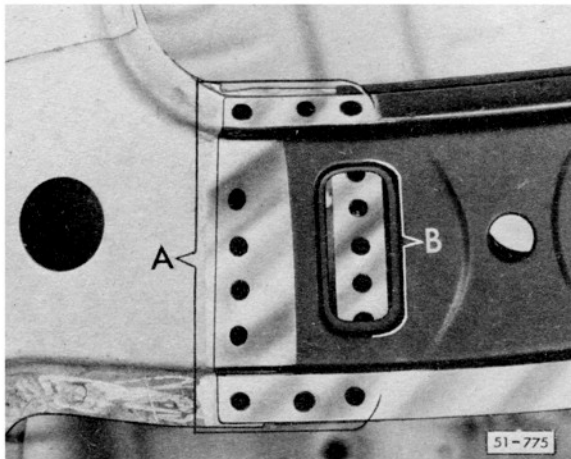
Querträger für Dach vorn einschweißen.
